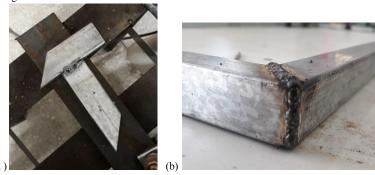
Em (a): tubo de aço furado devido a soldagem por eletrodo revestido; em (b): soldagem MIG/MAG.
